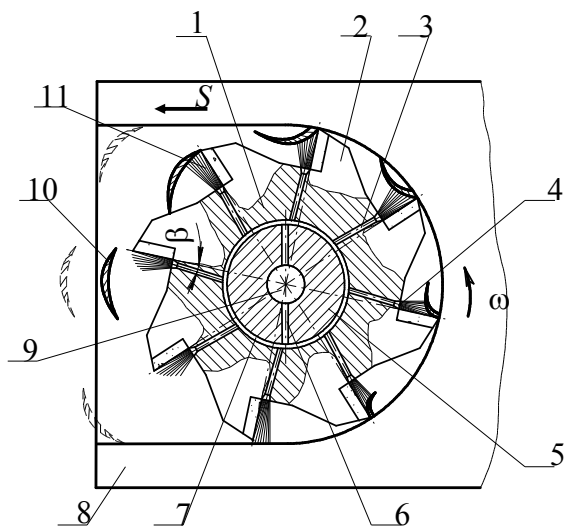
Фреза для обработки Т-образных пазов: 1 – корпус; 2 – зуб; 3 – канал в корпусе фрезы; 4 – насадок; 5 – оправка; 6 – радиальный канал; 7 – кольцевая проточка; 8 – обрабатываемая заготовка; 9 – осевой канал; 10 – элемент стружки; 11 – струя рабочей смеси
